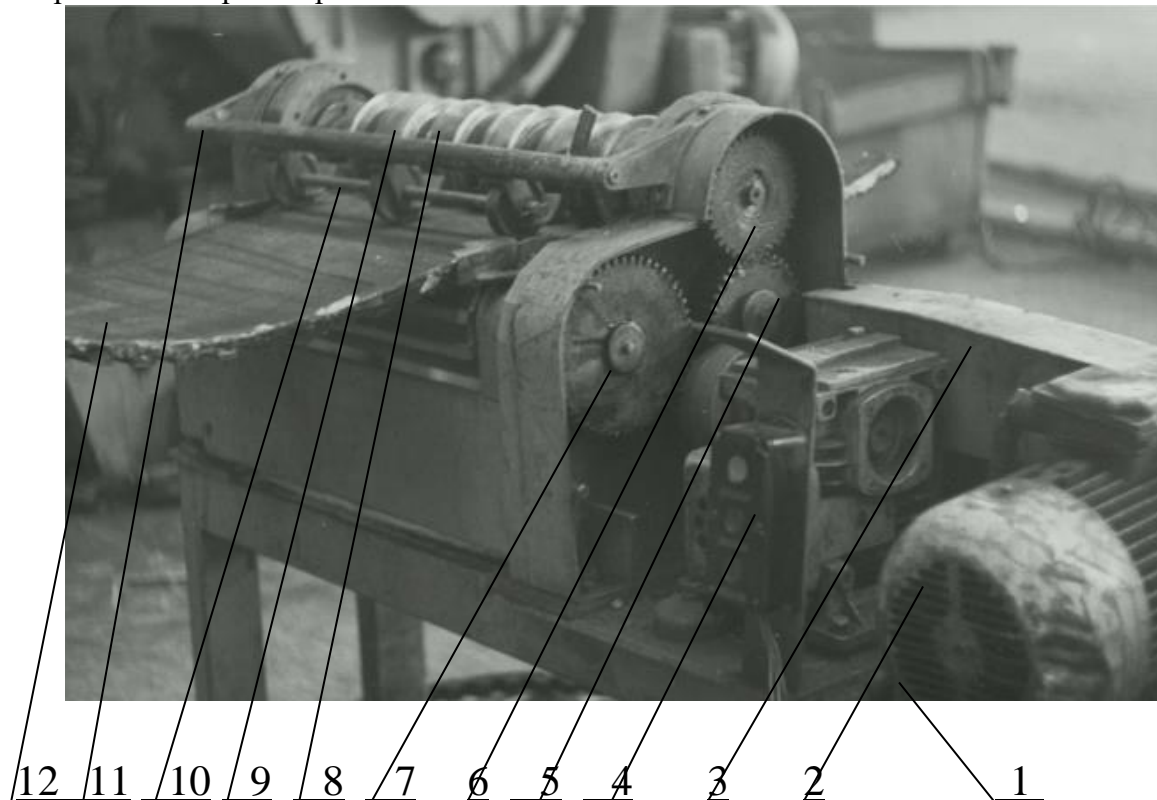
Загальний вигляд установки для розрізання конвеєрної стрічки з 5 ножовими блоками
